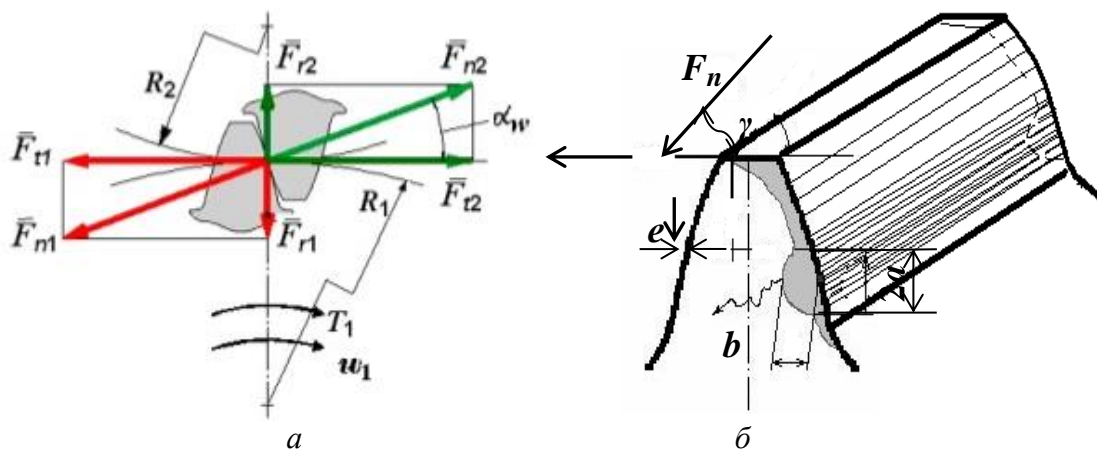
Сили зачеплення в циліндричній зубчастій передачі (а); і еюра зносу зуба шестерні циліндричній зубчастій передачі (б)
